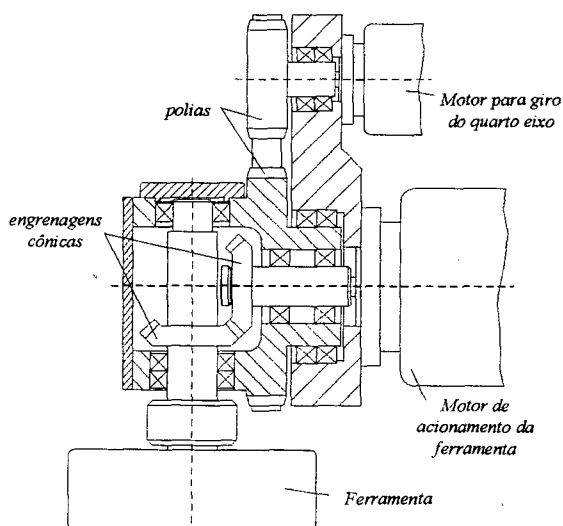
Sistema mecânico baseado em engrenagens cônicas.
